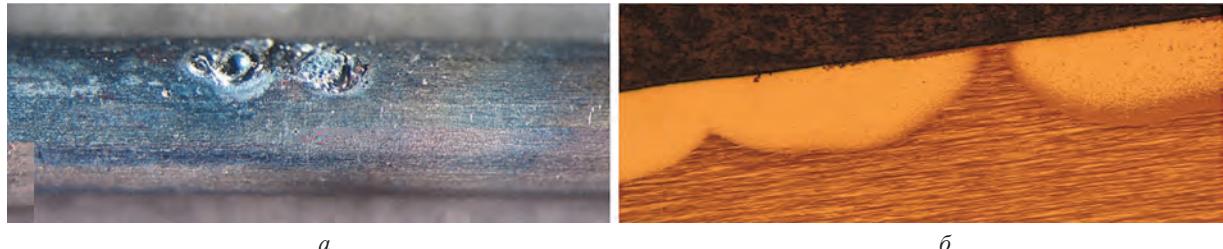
Внешний вид (а) и микроструктура (б) проволоки с дефектом сварного шва «искрение» (травление в реактиве «Нитал»)
